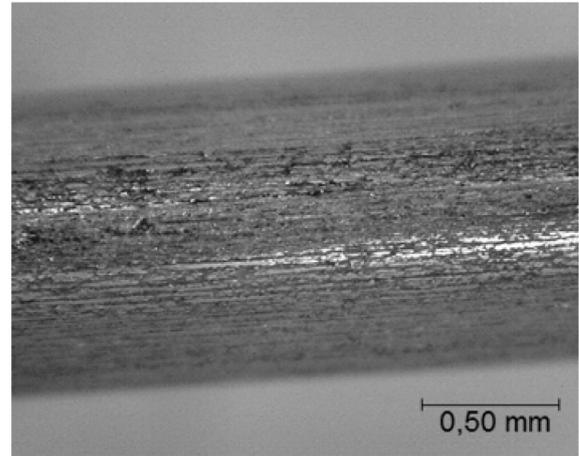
Verkupfertes Schweißdraht SG, Lieferzustand
